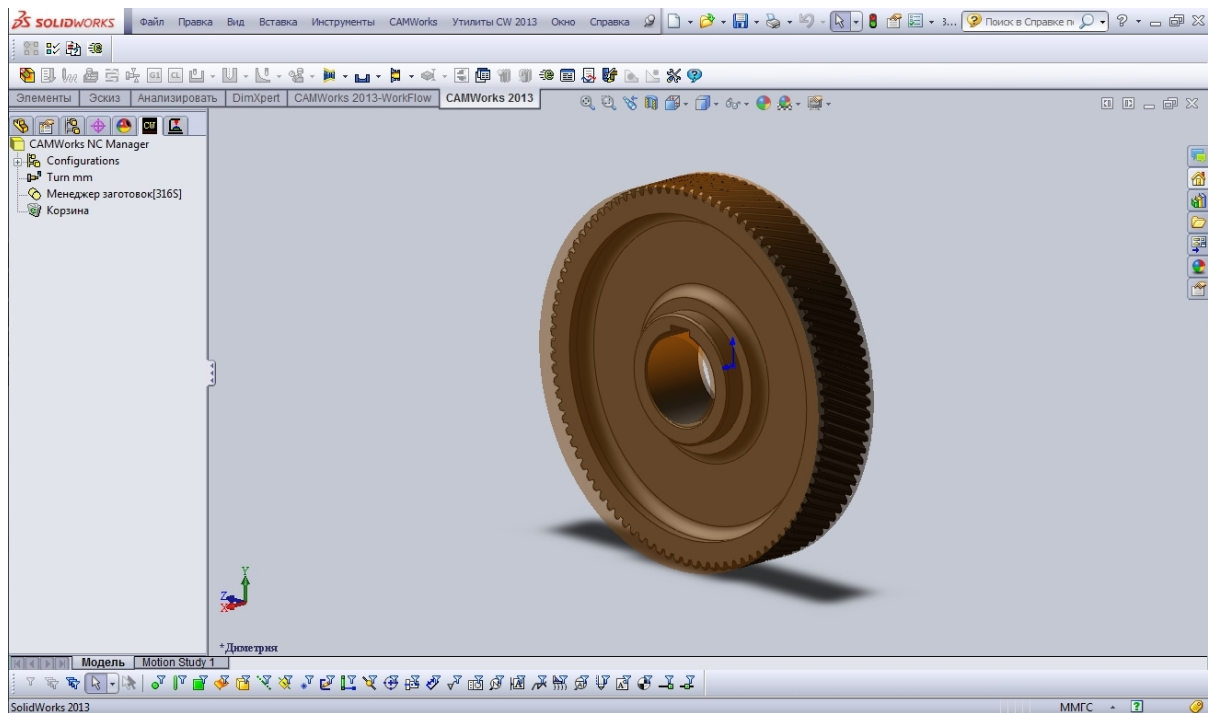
Ескіз заготовки (прозора) з деталлю «Колесо ТП 05.22.05.196.003» в CAMWorks
